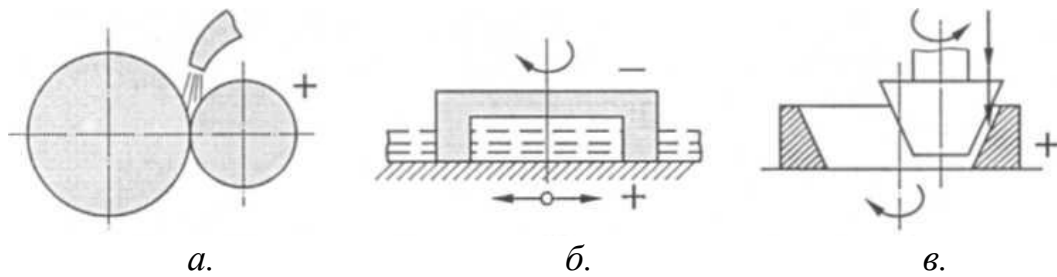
Електроерозійне шліфування поверхонь деталей
